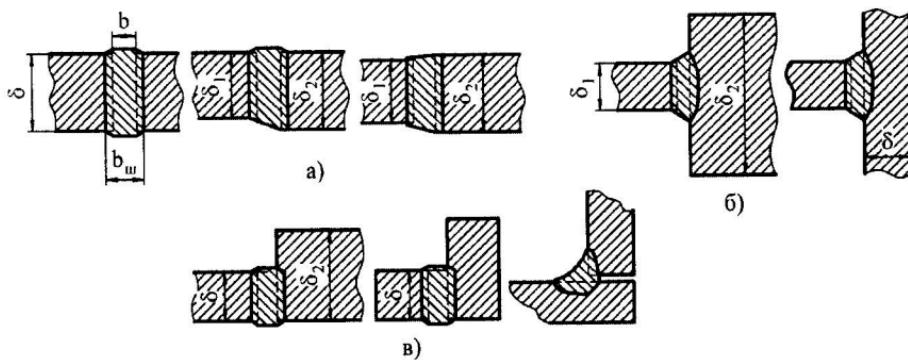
Види з'єднань, виконаних електрошлаковим зварюванням: а) – стикові, б) – таврові; в) – кутові; д – товщина металу; b – ширина зазору; b_w - ширина шва
